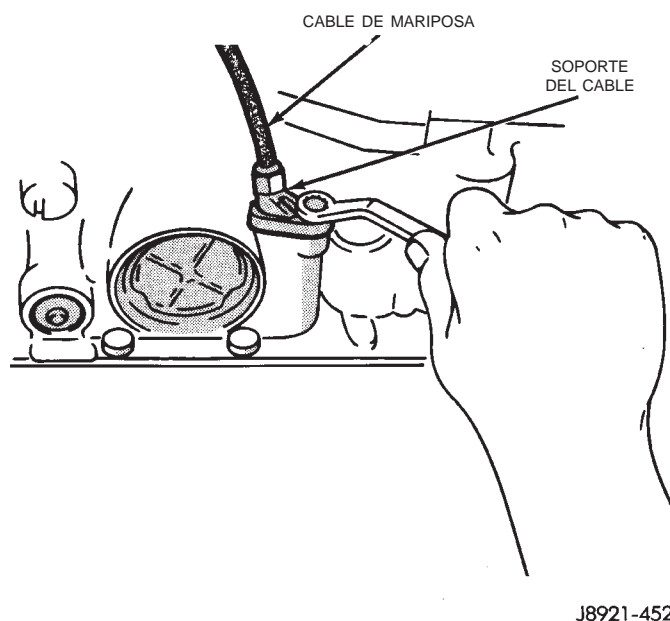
Desmontaje e instalación del cable de mariposa y soporte de la transmisión
